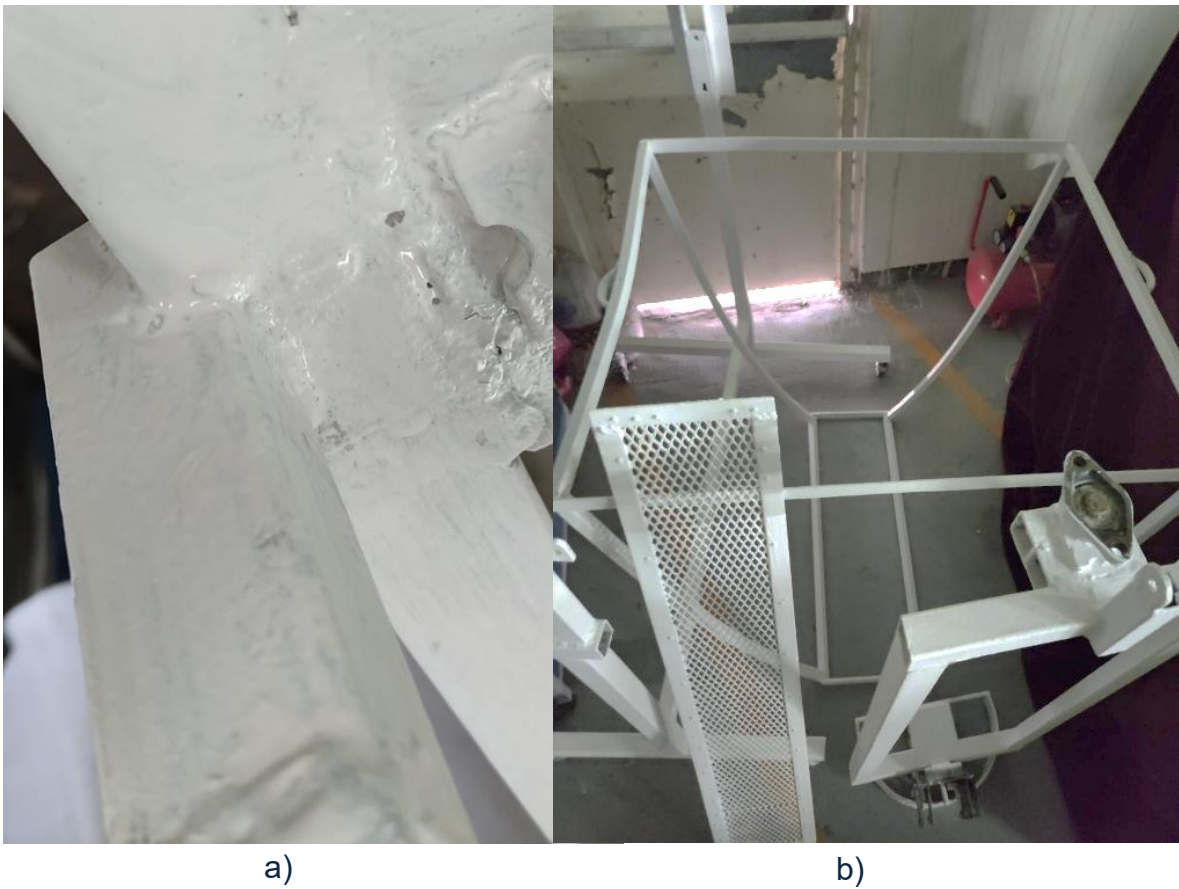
Estructura metálica del CPC 2 con: a) primera aplicación y b) segunda aplicación de imprimación.
